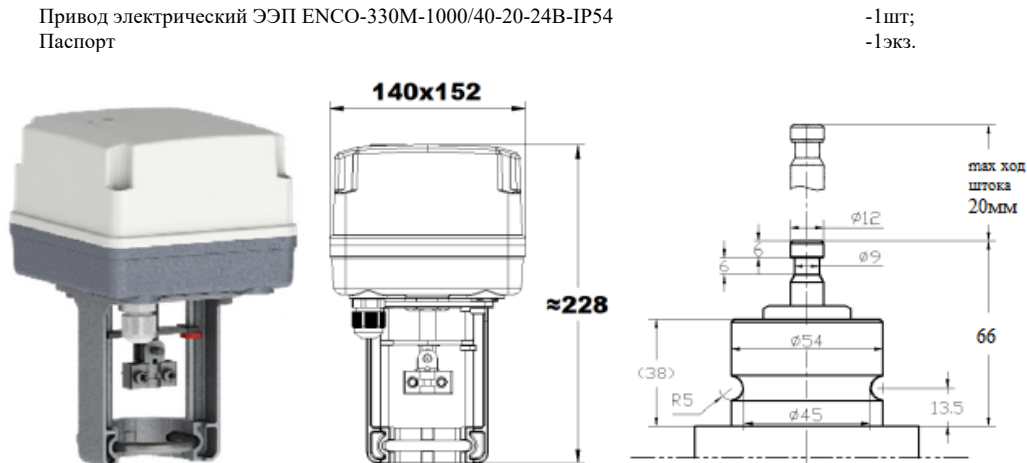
Габаритные размеры Э/П ENCO-330M-1000/40-20-24V-IP54
